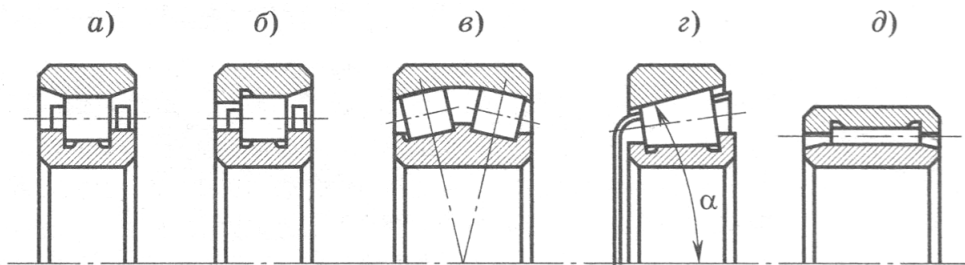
Роликовые подшипники качения: *a, б* – радиальные с короткими цилиндрическими роликами; *в* – радиальный сферический двухрядный; *г* – конический однорядный; *д* – игольчатый
